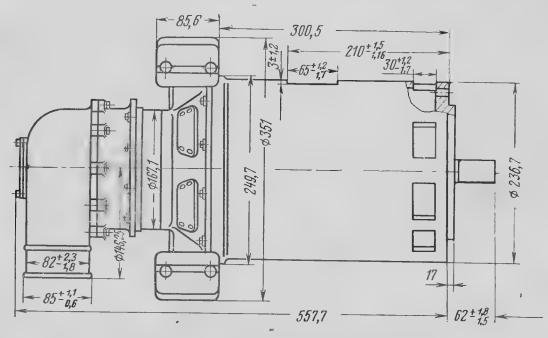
Габаритные и установочные размеры генератора СГС-90/360 2с
